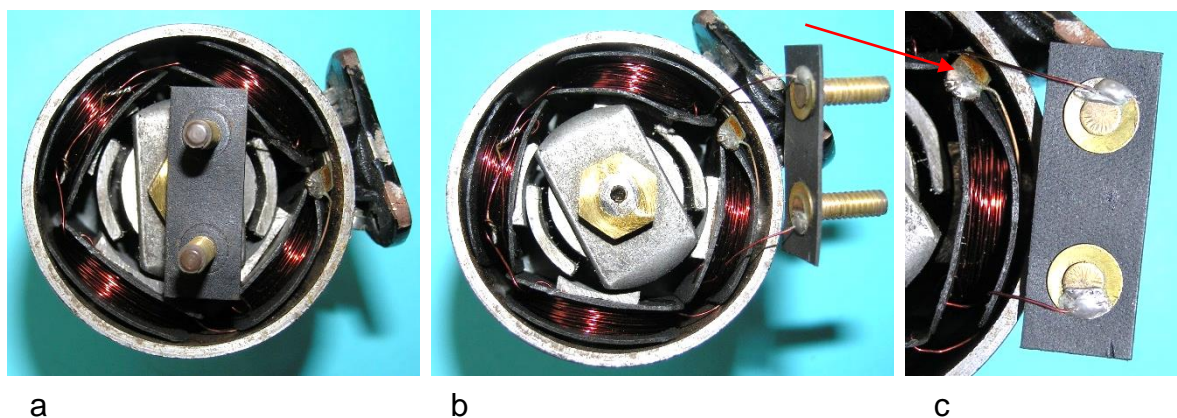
Generator: a) Anker mit zwei Kabelanschlussbolzen, b) Polrad in der Ankerbohrung, c) Lötstellen am Gehäusemantel und an den Kabelanschlussbolzen
